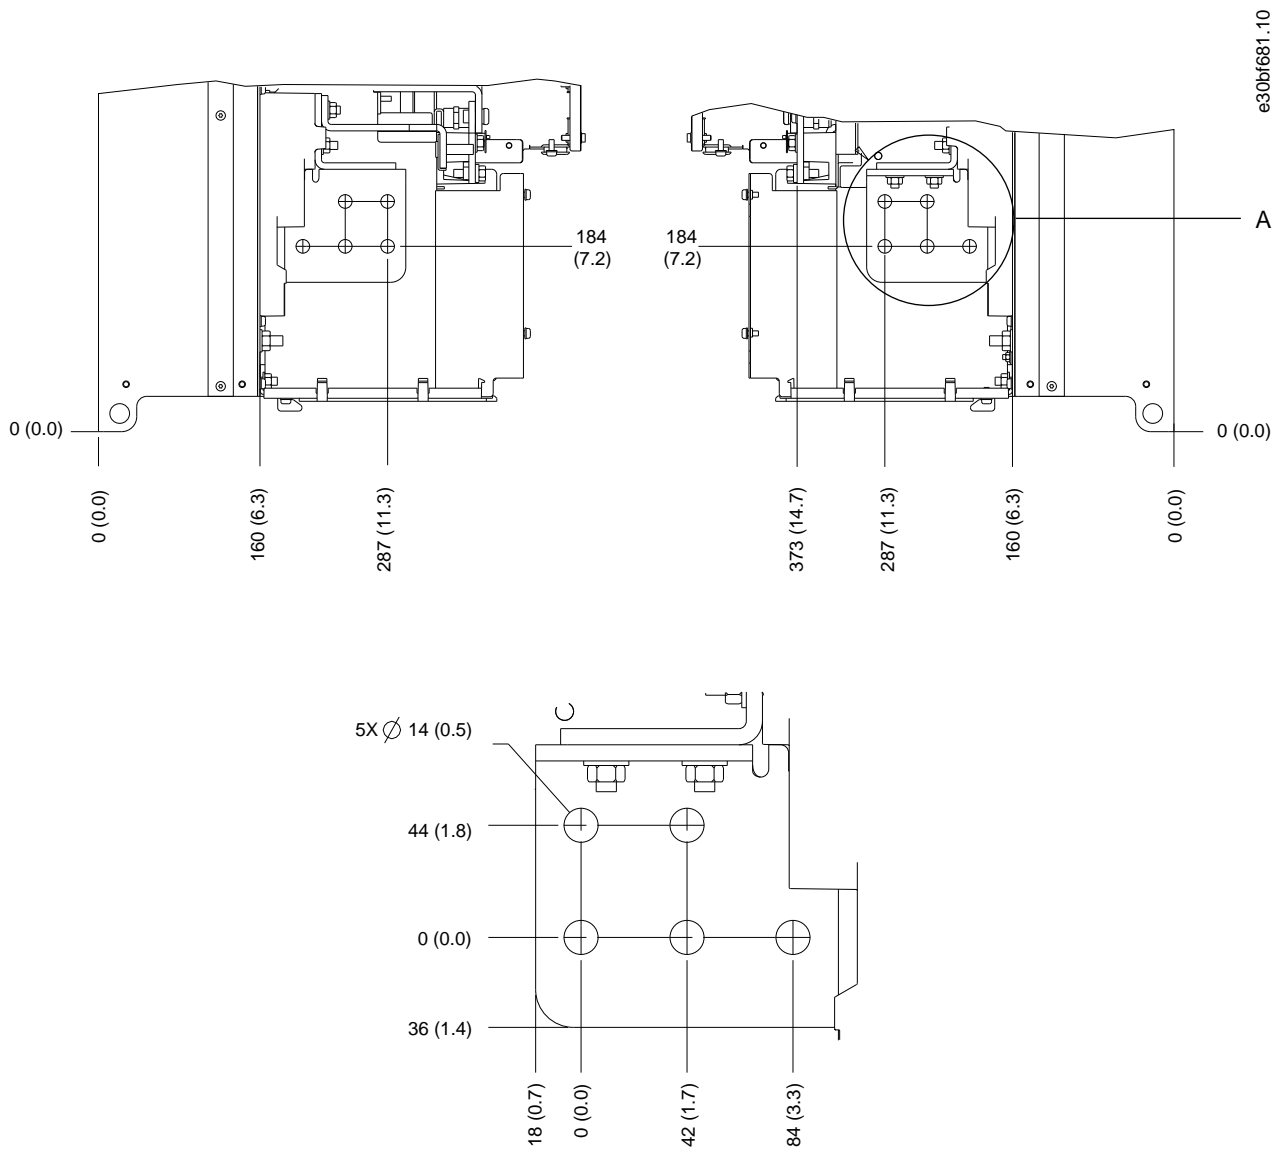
Dimensions des bornes réseau, moteur et de terre E4h (vues latérales)
